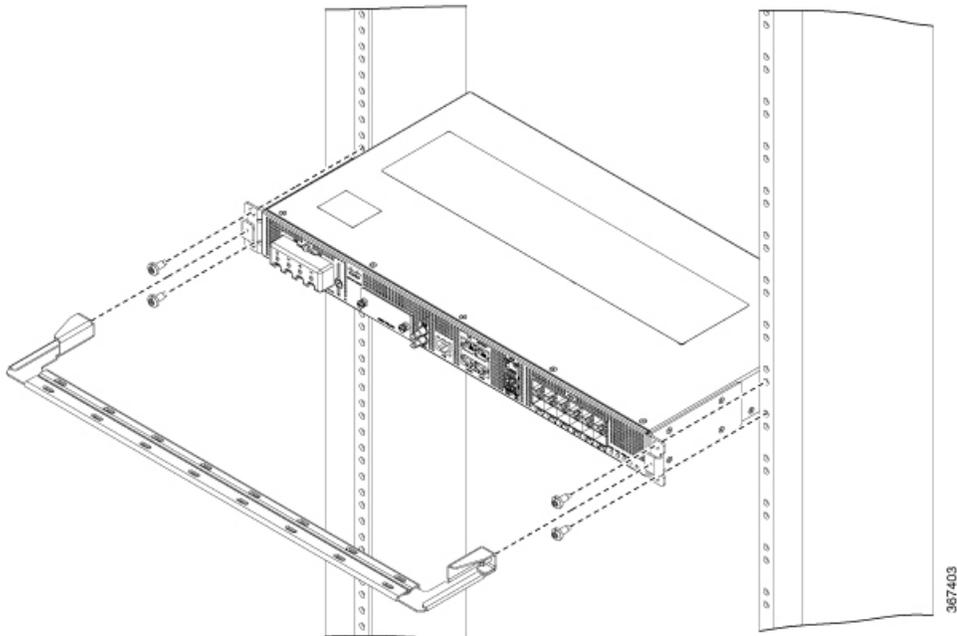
Dispositif de fixation central avec guide-câble sur un rack de 19 pouces
